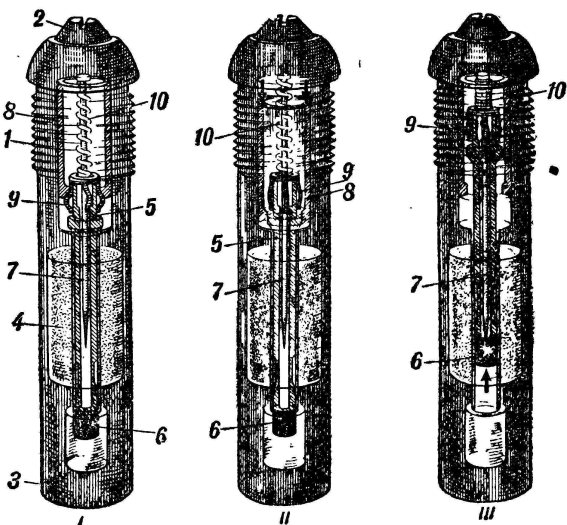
Схема взрывателя УГТ. I — положение подвижных частей взрывателя до выстрела; II — в момент выстрела, III — в момент удара снаряда в преграду; 1 — корпус взрывателя; 2 — головка; 3 — дно; 4 — детонатор (взрывчатое вещество); 5 — ударник; 6 — капсюль; 7 — жало; 8 — оседающий цилиндр; 9 — предохранитель; 10 — пружина.
